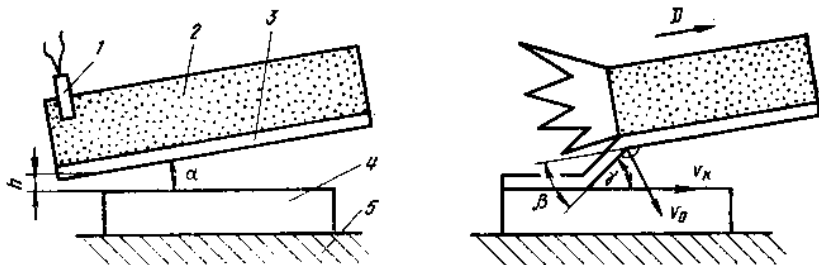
Схема сварки взрывом под углом:
